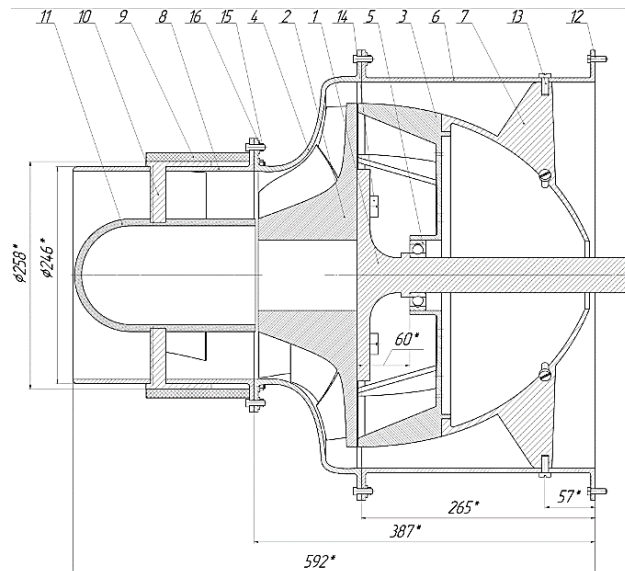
Модернізований ВВ вертольоту Мі-2: 1 – вал; 2 – відцентрове колесо; 3 – диск статора; 4 – дифузор; 5 – керамічний підшипник; 6 – корпус; 7 – конус дифузора; 8 – корпус обтічника; 9 – кожух; 10 – лопать статора; 11 – обтічник; 12 – болт; 13, 14 – гвинти; 15 – гайка; 16 – шайба.
